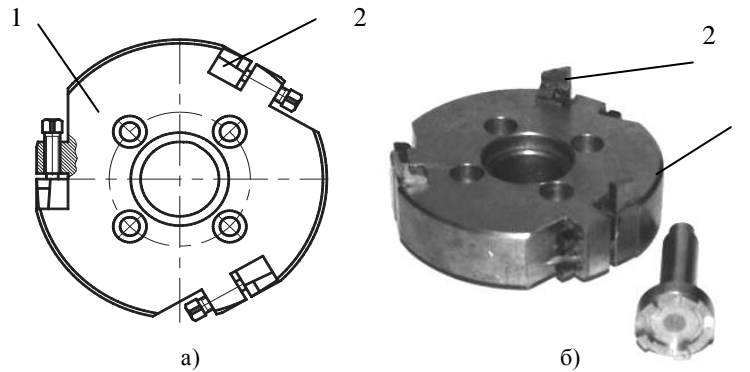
Инструмент к станку модели ВС-50 для обработки торцового зубчатого контура:
